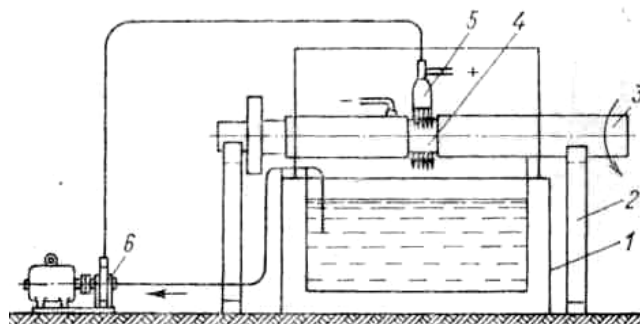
Схема установки для струйного нанесения покрытий:
